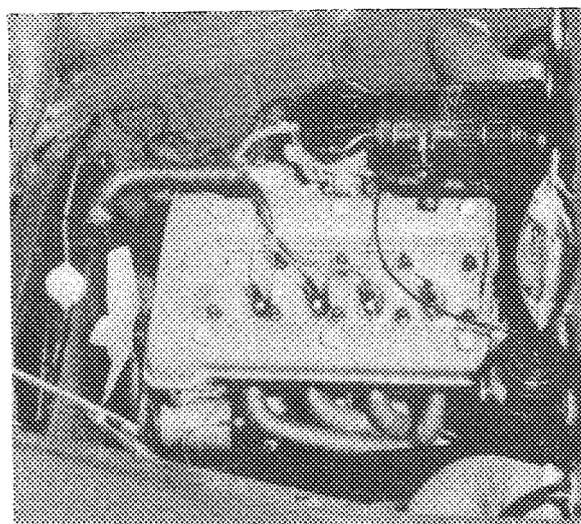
Foto O - Vista dall'alto del motore montato su vettura (con cofano aperto o tolto).
